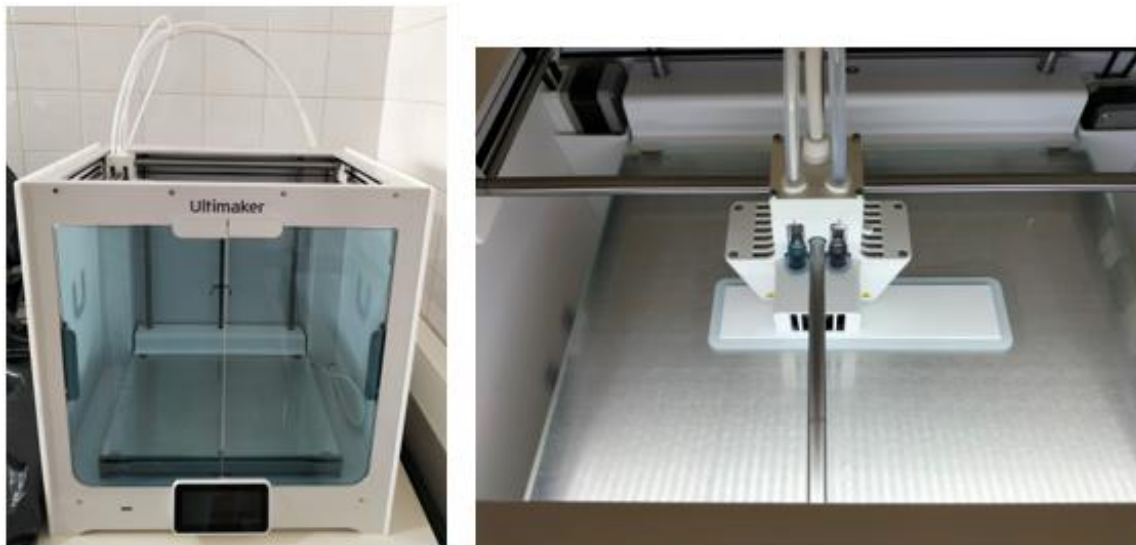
Impressora 3D Ultimaker S5 (esquerda) e impressora a imprimir um provete (direita)
